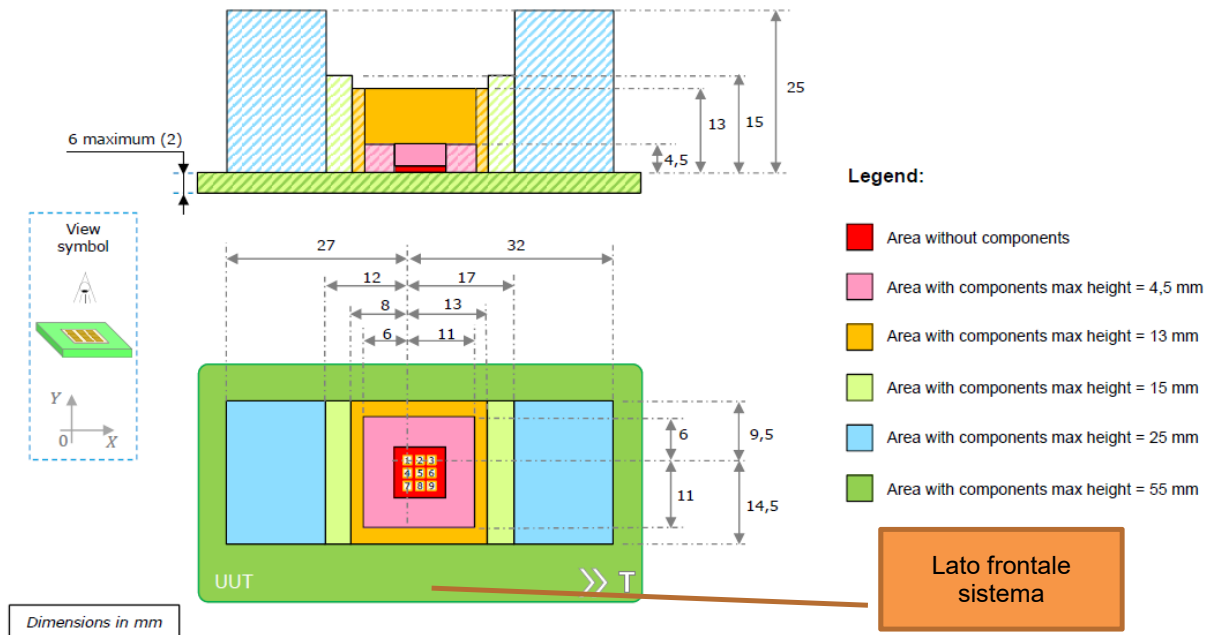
Dimensione della pad e layout lato superiore 1 e 4 MPU [dimensioni in mm]
